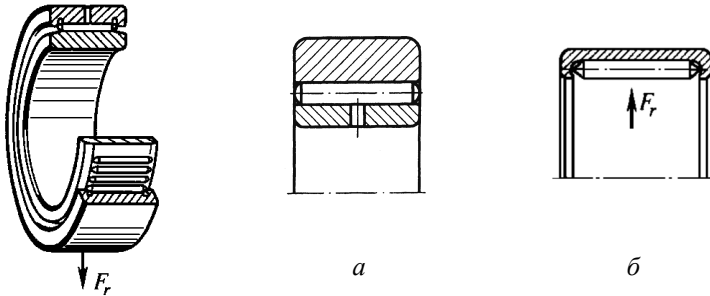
Роликовые радиальные подшипники с игольчатыми роликами
